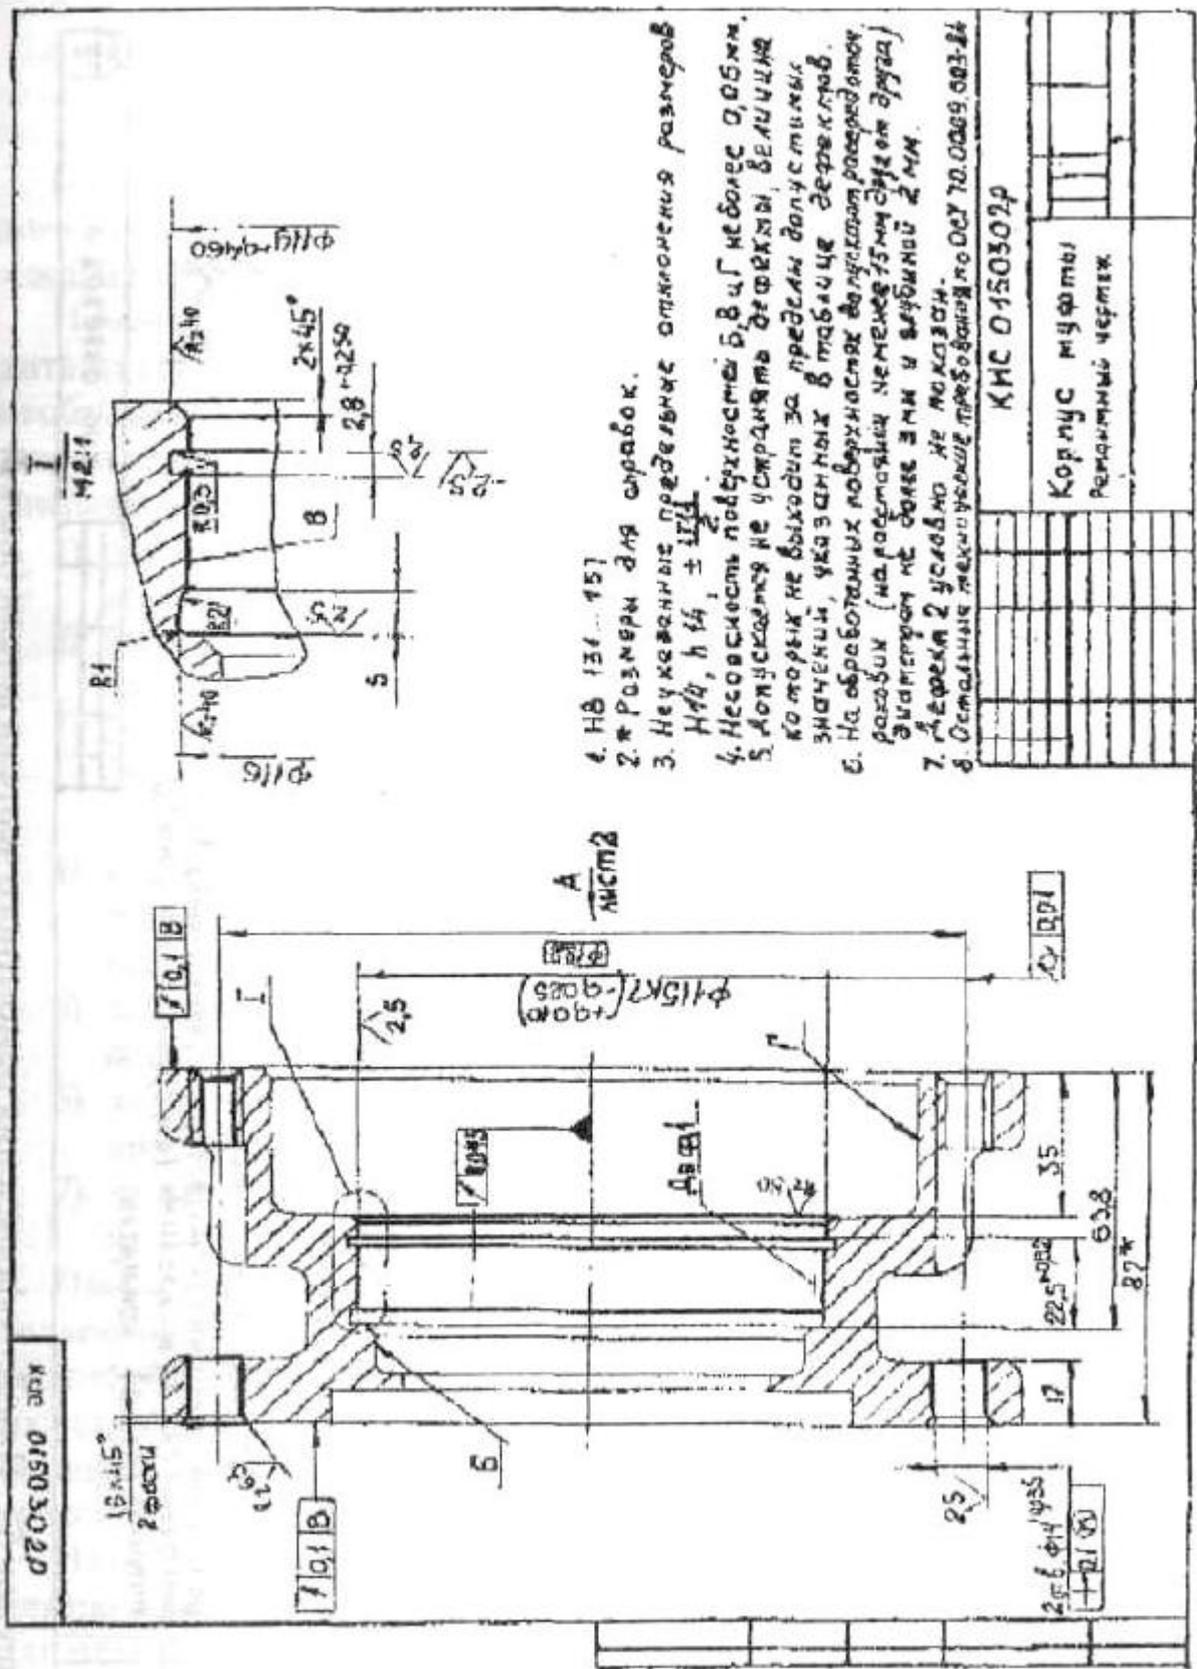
Пример оформления ремонтного чертежа детали (лист 1)
